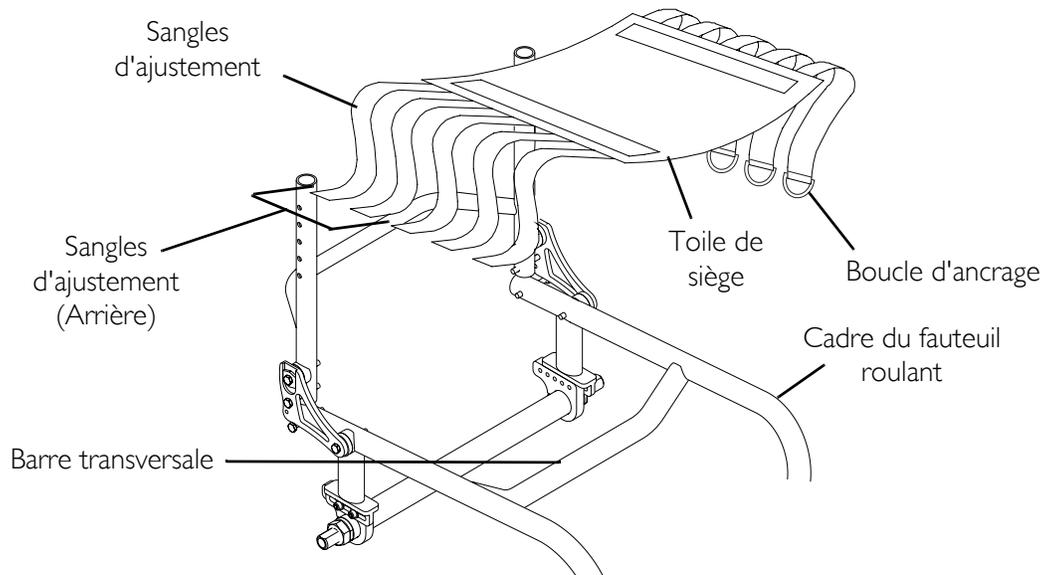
Remplacement de la toile de siège réglable en tension
